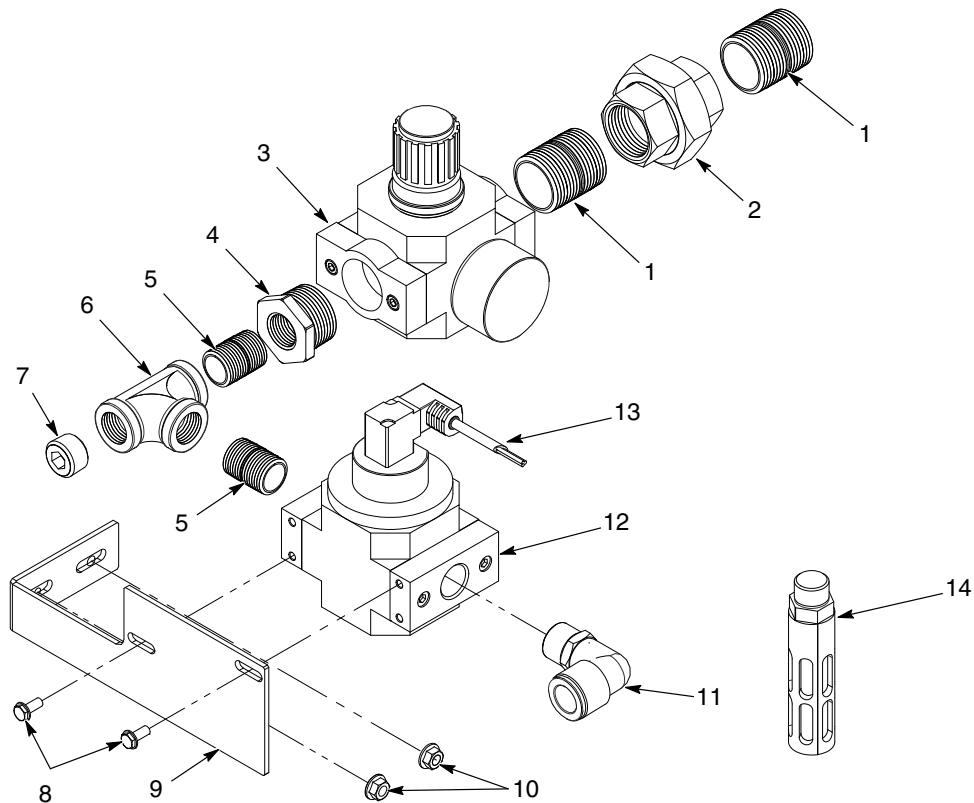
Spülventilbaugruppe - Konfiguration mit einer Lanze
